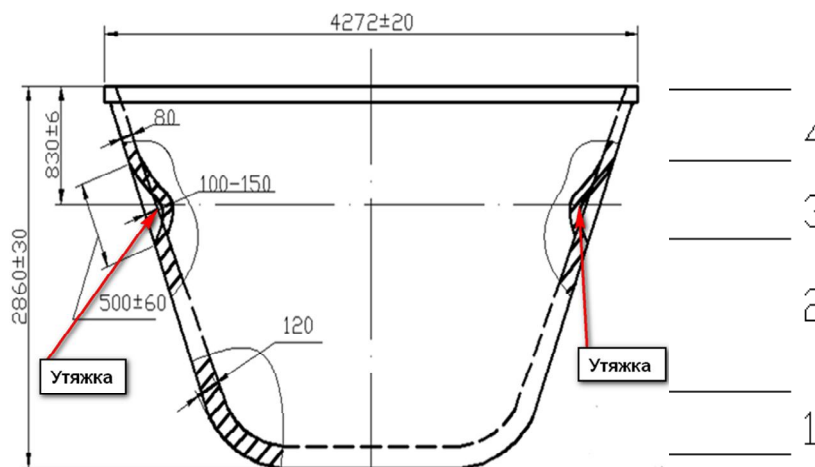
Эскиз чаши шлаковоза с деформированной стенкой: 1 – зона донной части чаши; 2 – зона боковой поверхности; 3 – зона образования утяжки; 4 – зона поверхности чаши выше утяжки
